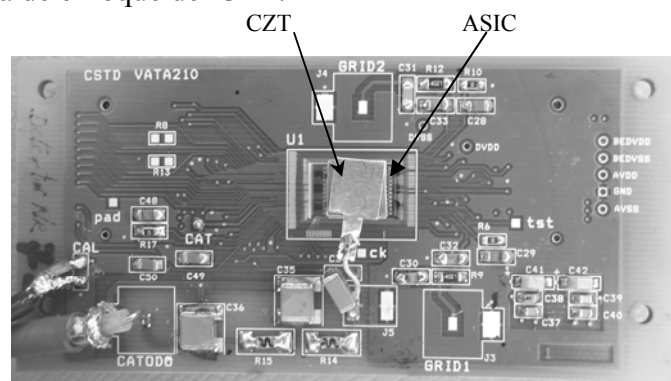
Fotografía de la tarjeta FEE con el detector y el ASIC soldados por medio de esferas.
